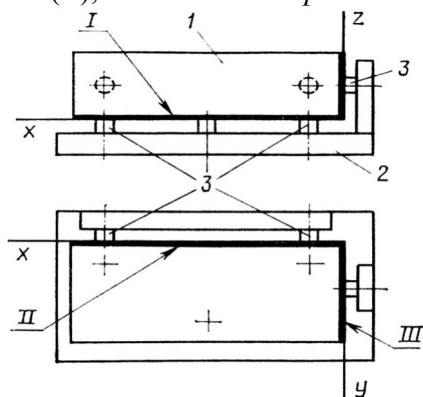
Базы поверхні: I – основна; II – напрямна; III – опорна;
